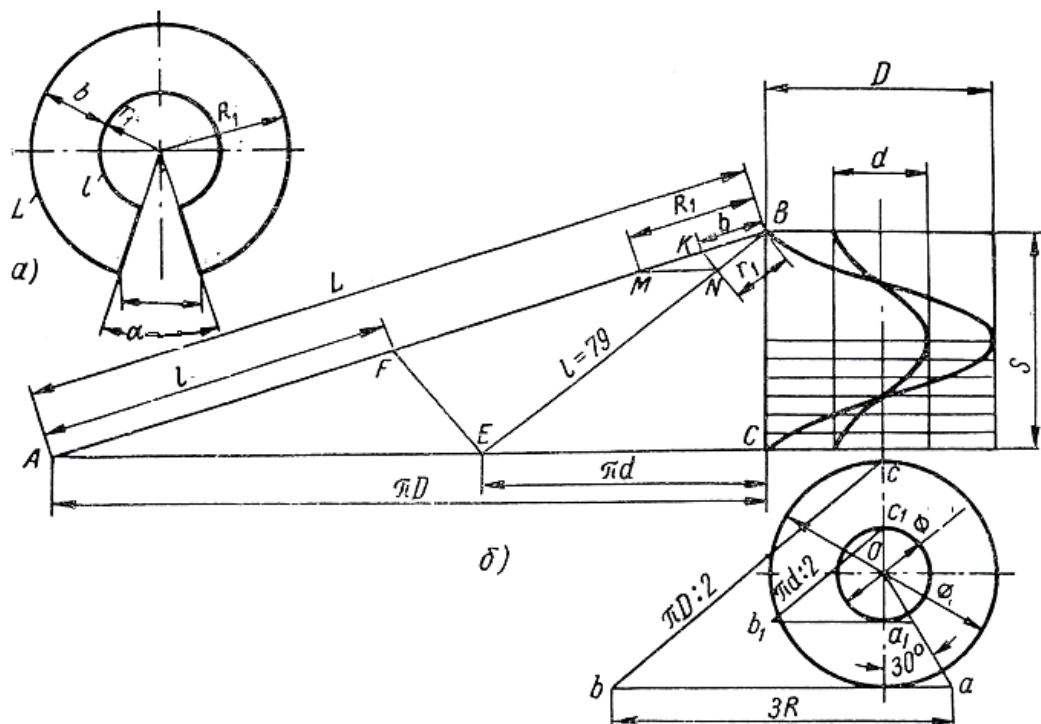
Схема до розрахунку розгортки витка шнека
